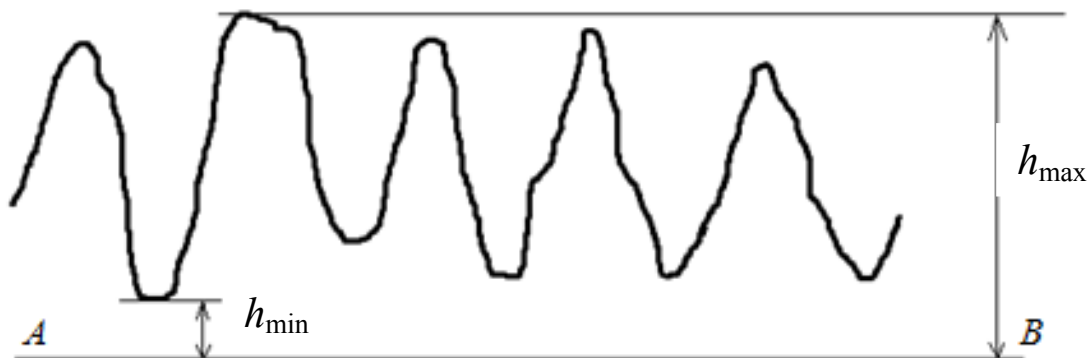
Схема шероховатости поверхности и ее элементы
